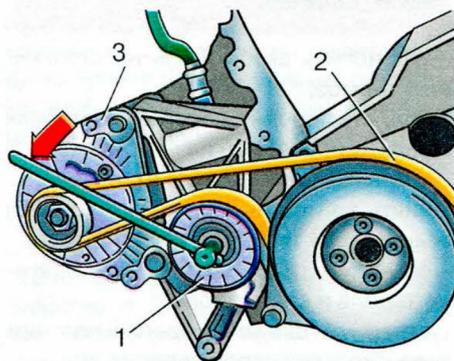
Привод генератора 4-цилиндрового дизельного двигателя: 1 – ролик механизма натяжения ремня; 2 – ремень привода генератора; 3 – генератор
